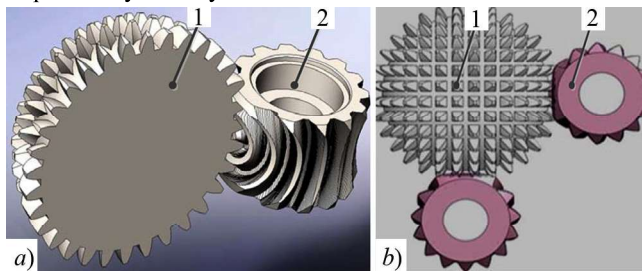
3D зображення шестерень технології Abenics / 3D image of ABENICS technology gears: 1 – сферична шестерня / spherical gear; 2 – шестерня-монополь / monopole gear
